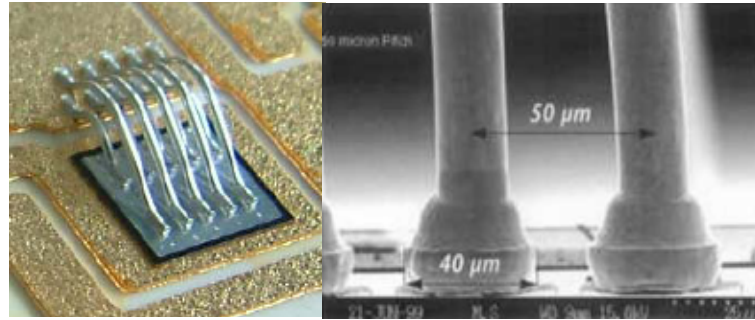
Photo de fils d’aluminium dopé nickel assemblé par *wedge bonding* [Amr06] à gauche et d’un fil d’or assemblé par *ball bonding* [sil11] à droite.
